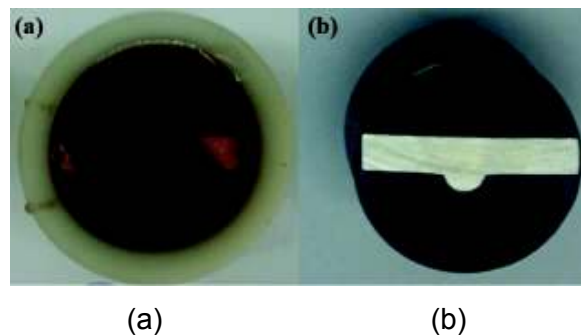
Probeta para el ensayo metalográfico a) Moldeado de la probeta y b) Probeta montada.
